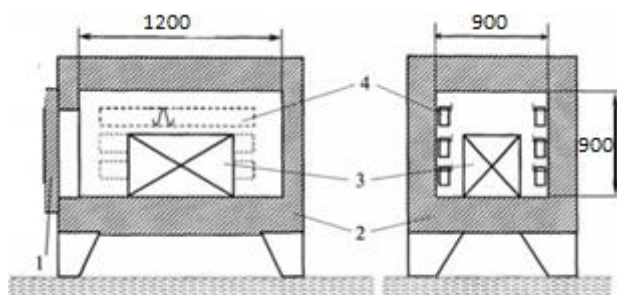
Камерная электропечь: а) вид сбоку; б) вид спереди; 1 — дверца; 2 — футеровка; 3 — изделие; 4 — нагреватель. Принимаем схему соединения нагревателей «звезда»
